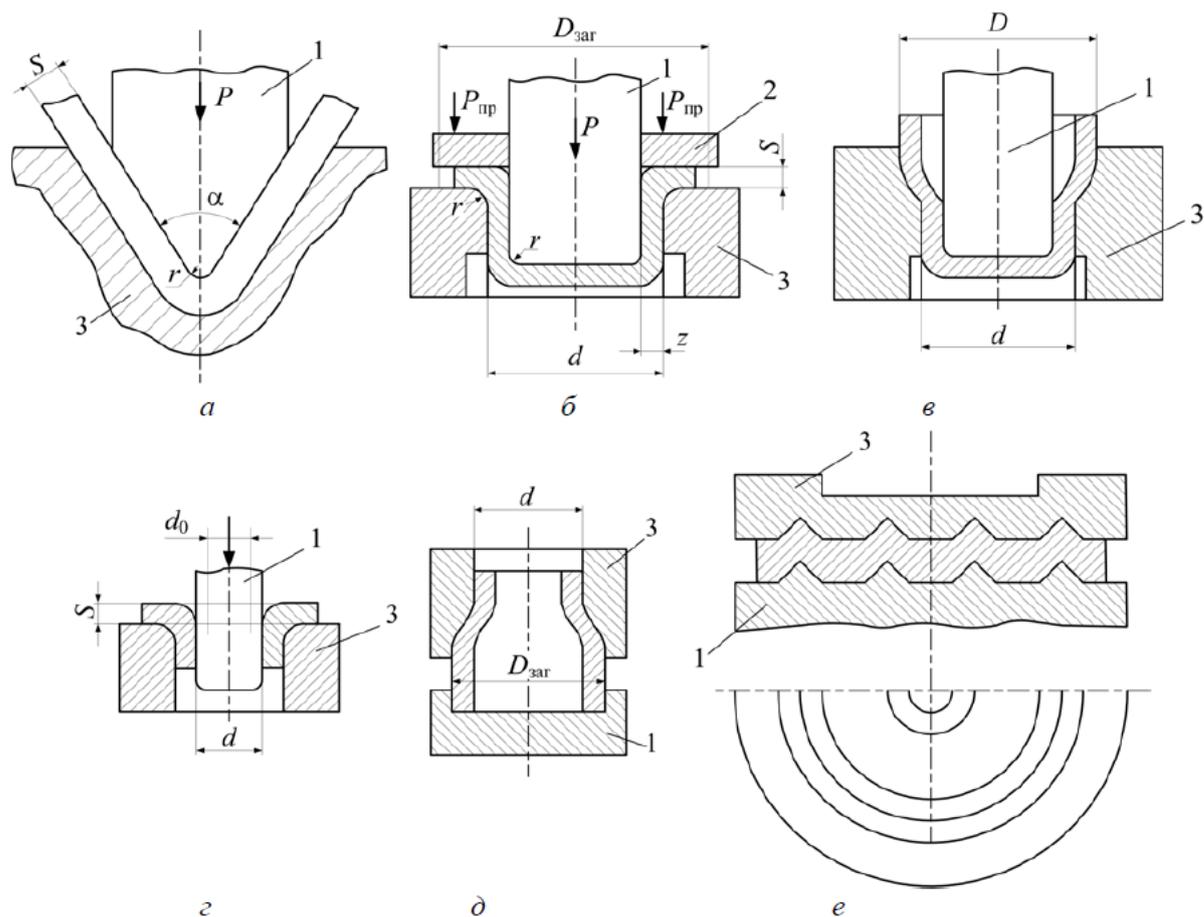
Формоизменяющие операции листовой штамповки: а – гибка; б, в – вытяжка; г – отбортовка; д – обжим; е – формовка; 1 – пуансон; 2 – прижим; 3 – матрица
